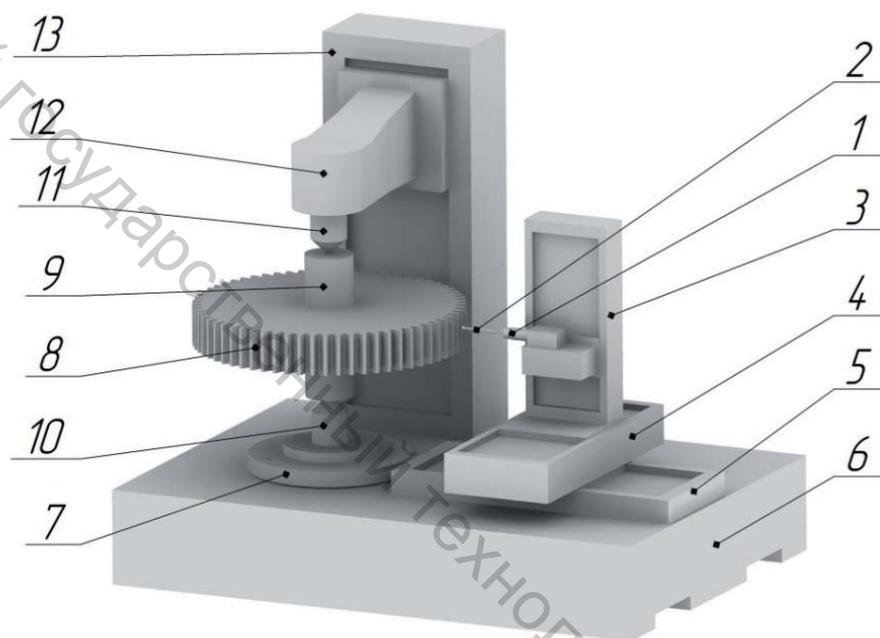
Комплекс для проверки параметров точности цилиндрических зубчатых колес
